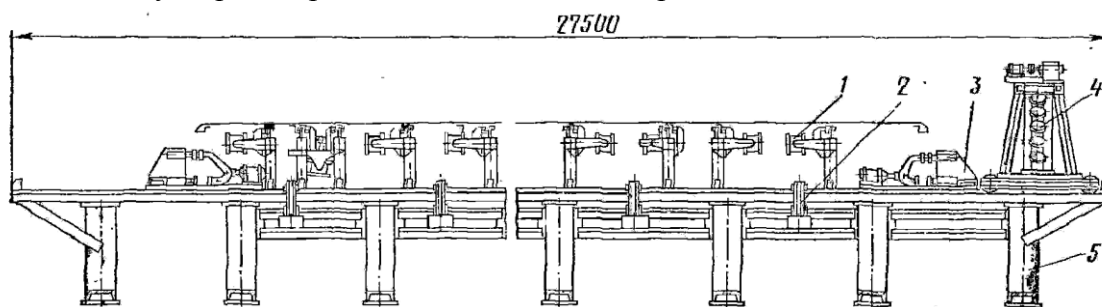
Кондуктор для сборки и сварки крыши кузова пассажирского вагона: 1 – пневматический прижим дуги крыши; 2 – прижим-фиксатор обвязочного угольника; 3 – упор концевой части крыши; 4 – передвижной портал с пневмоприжимами; 5 – рама кондуктора
